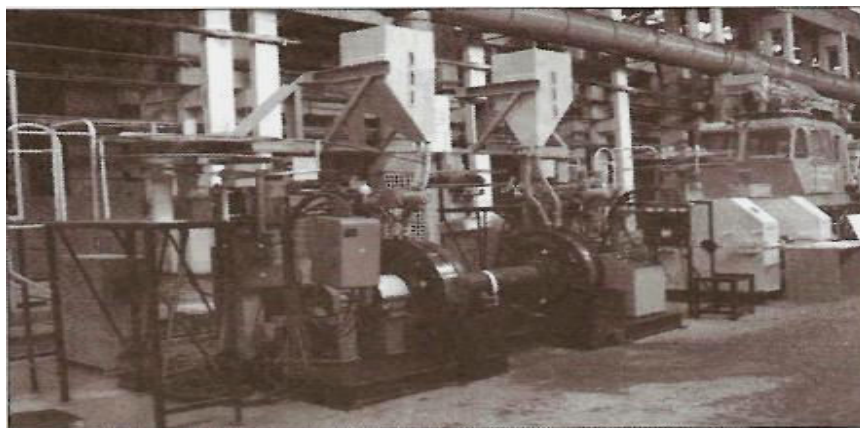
Установа ПКТБ ЦВ «Укрзалізниці» для двохелектродного наплавлення поверхні катання вагонних коліс [8]
